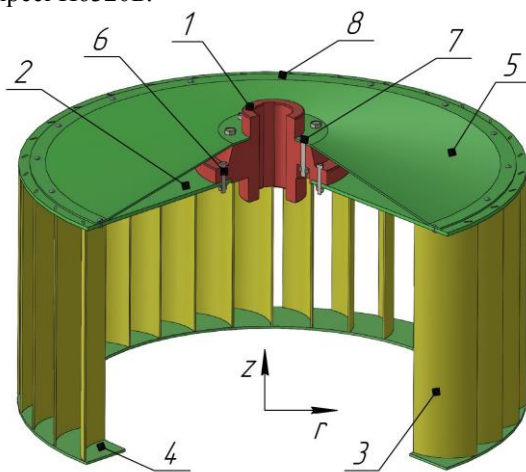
Загальний вигляд робочого колеса відцентрового вентилятора: 1 – ступиця; 2 – задній диск (кільцева пластина); 3 – лопаті; 4 – передній диск (кільце); 5 – конічна кришка (конічна оболонка); 6, 7 – болтові з'єднання із гайками; 8 – заклепкове з'єднання.
